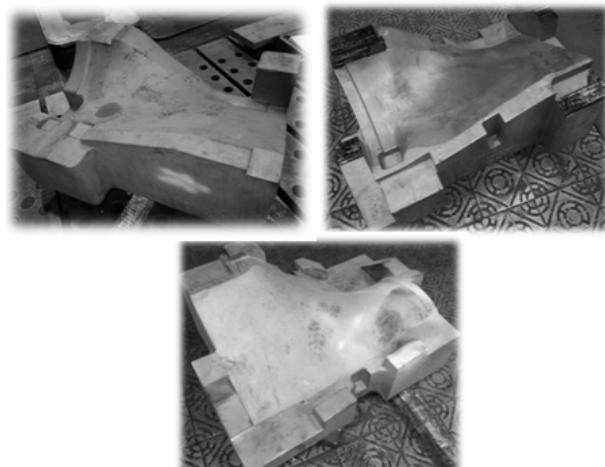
Жаропрочные заготовки штамповой оснастки, обрабатываемые на станках с ЧПУ
